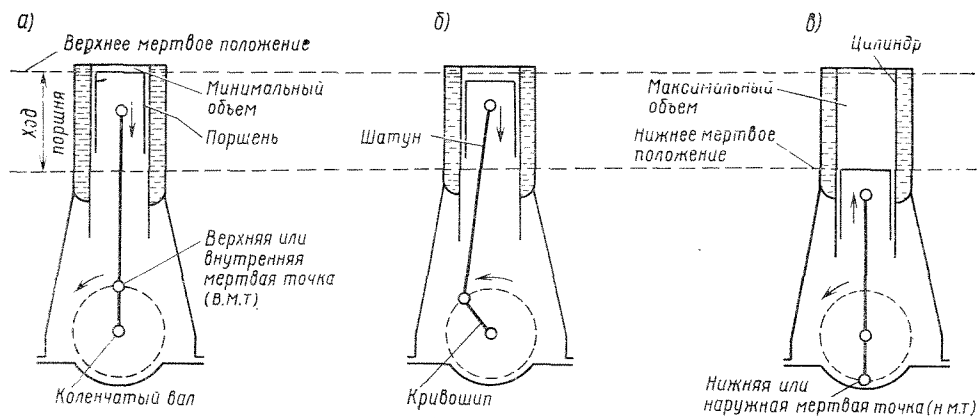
Схема шатунно-кривошипного механизма поршневого двигателя
